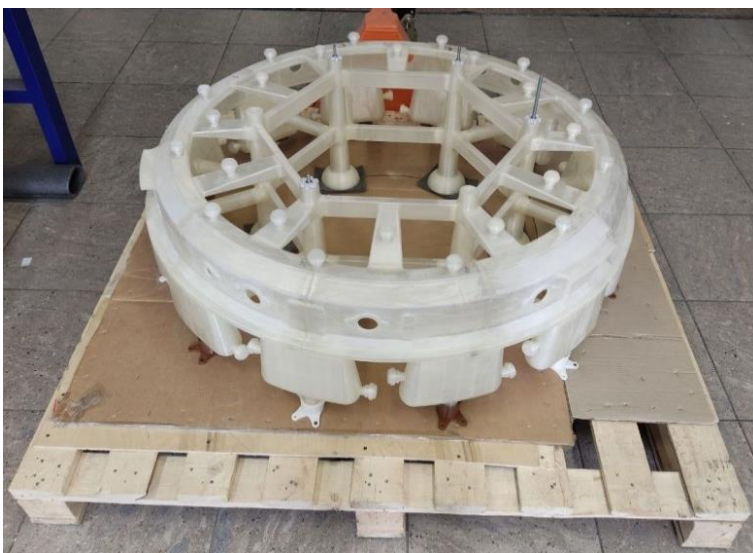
Выращенная модель отливки детали «Корпус наружный»
